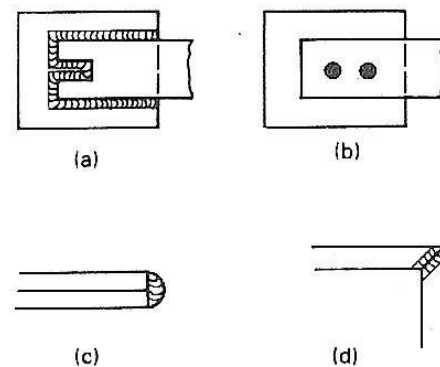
(a) Soldadura de ranura o de muesca, (b) soldadura de tapón, (c) soldadura de borde, (d) soldadura en esquina.
